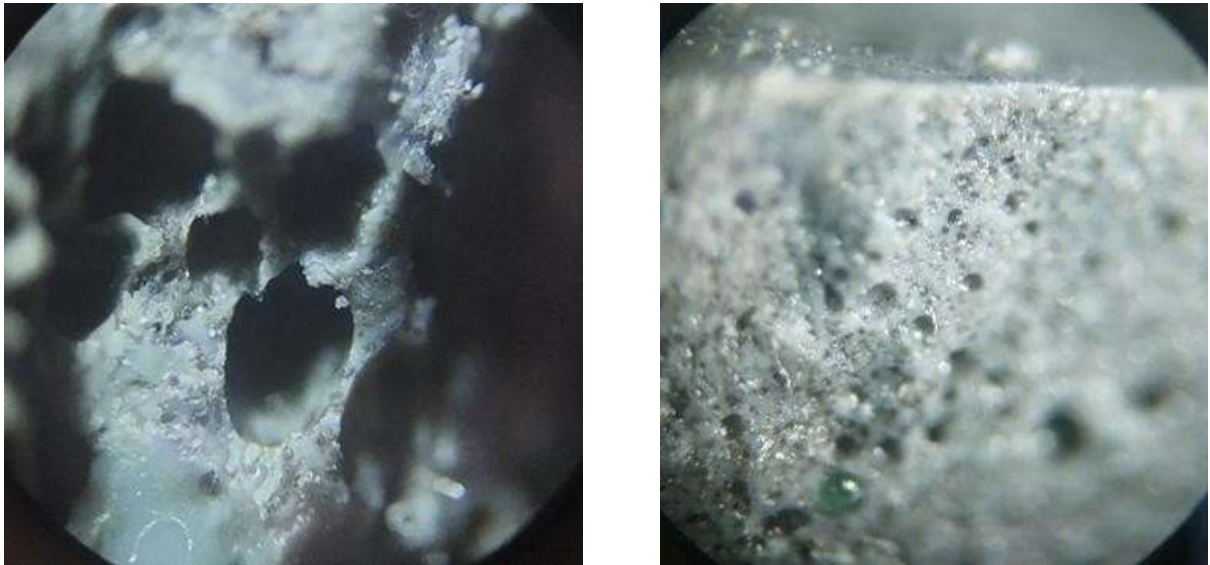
la fracture d'une éprouvette du mélange industriel (80%PETr/20%PEHDr)
